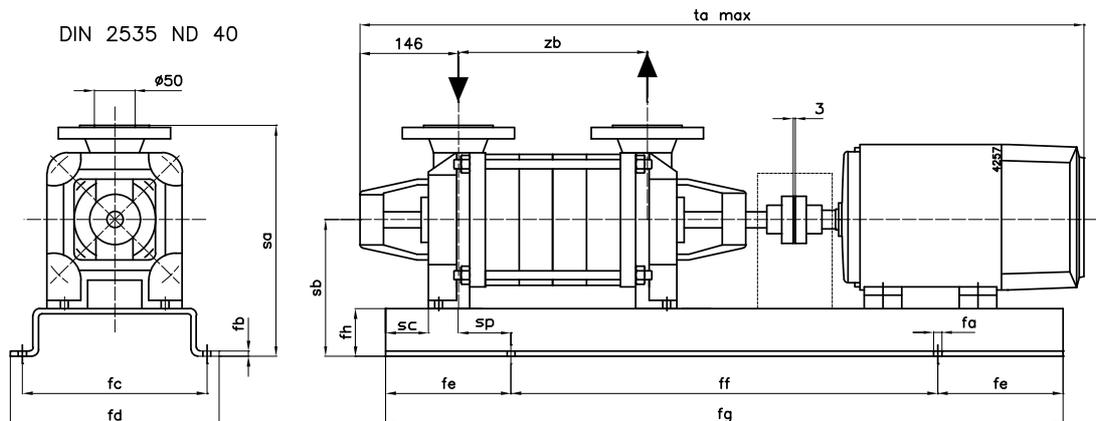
Dimensioni pompa con motore MCHZ(S) 14b.
